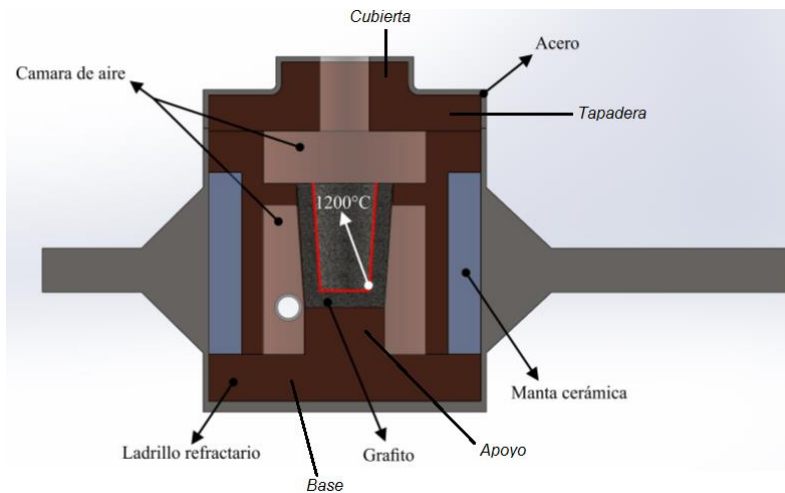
Vista en corte de perfil frontal del horno de crisol basculante y sus partes. Fuente: Autor
